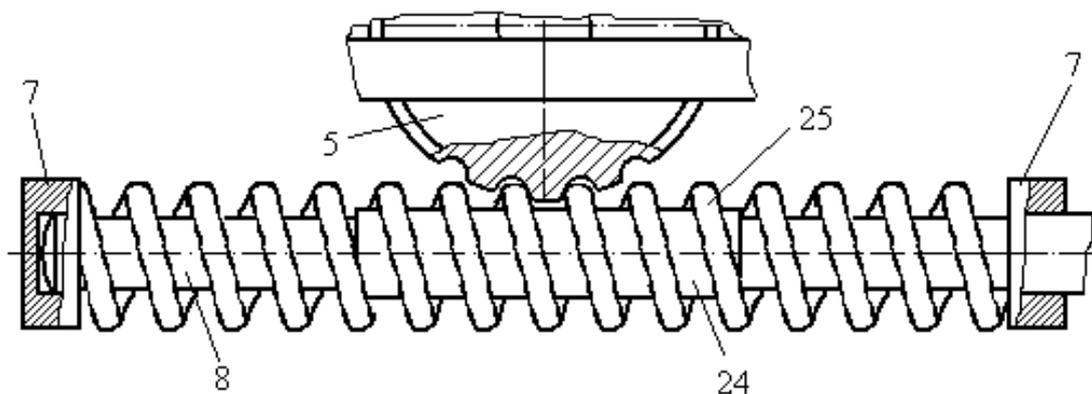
Схема привода с червяком, выполненным в виде вала с охватывающей его пружиной
